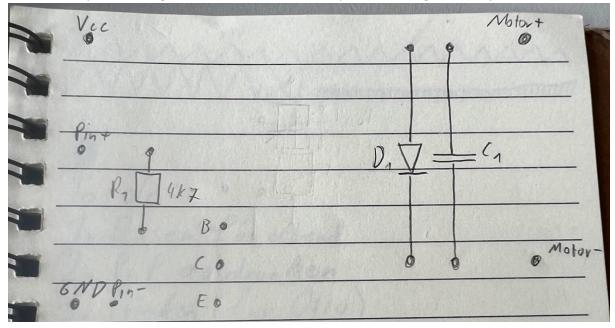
Layout der Lochrasterplatine für die Motorsteuerung
